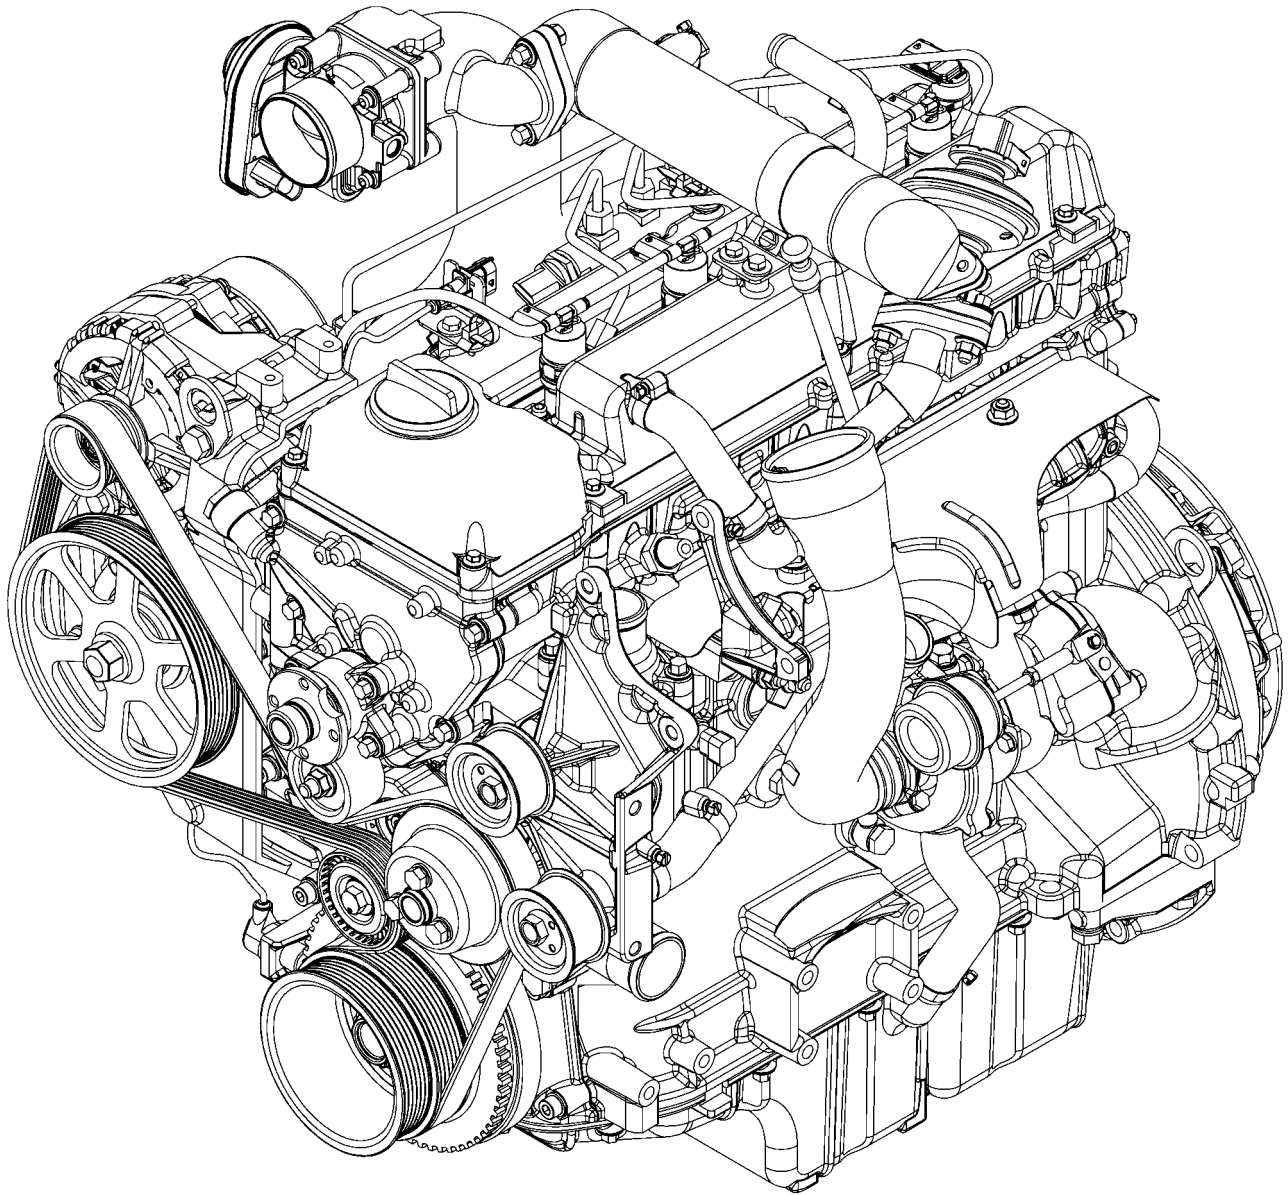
а. Внешний вид двигателя без компрессора кондиционера, насоса ГУР и деталей привода вентилятора
